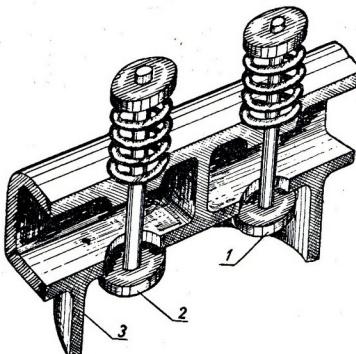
Головка двигателя с клапанами: 1 — выпускной клапан, 2 — всасывающий клапан, 3 — головка.
